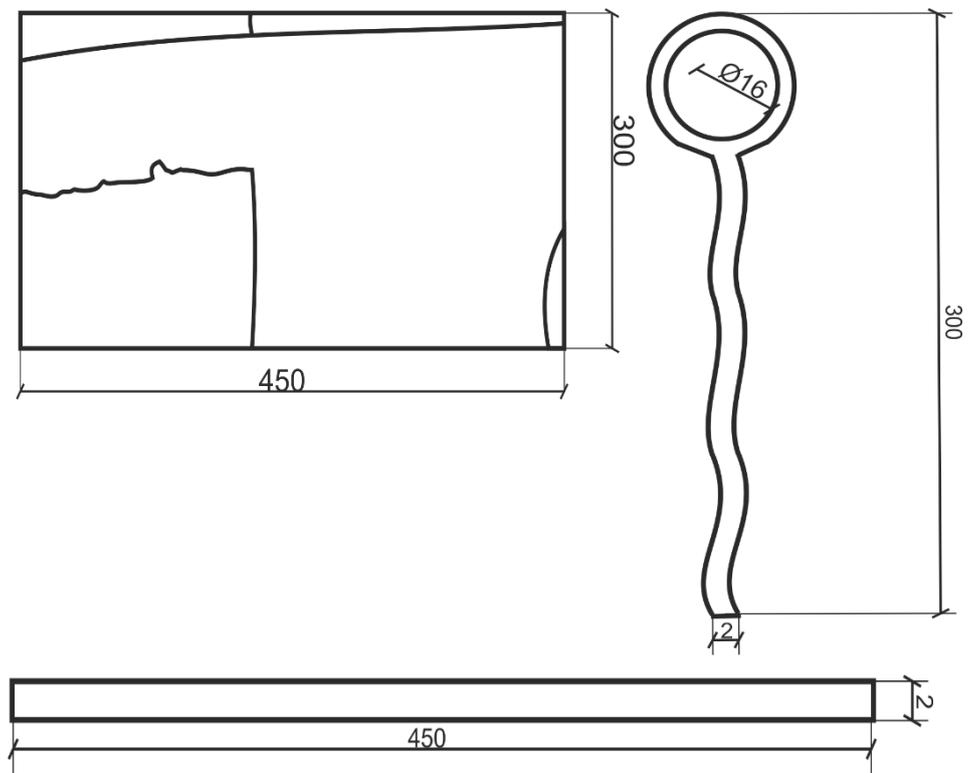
Mapa de medias. Alzado, perfil y planta de la pieza 4.
